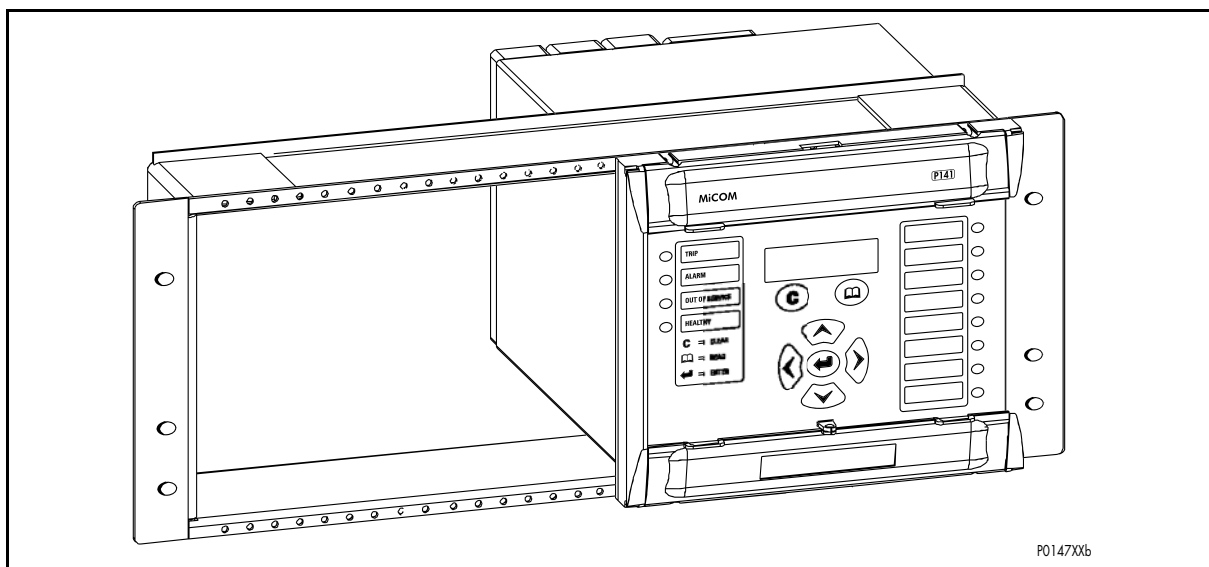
MONTAGE DES EQUIPEMENTS EN RACK
